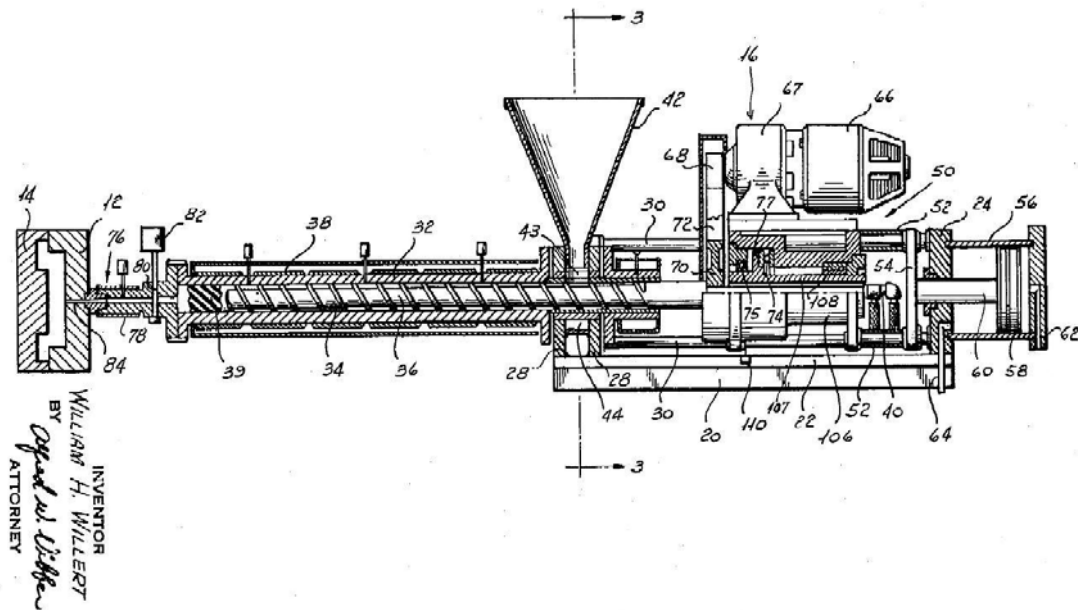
Disegno della macchina ad iniezione di Willert (fonte: www.avplastics.co.uk)
